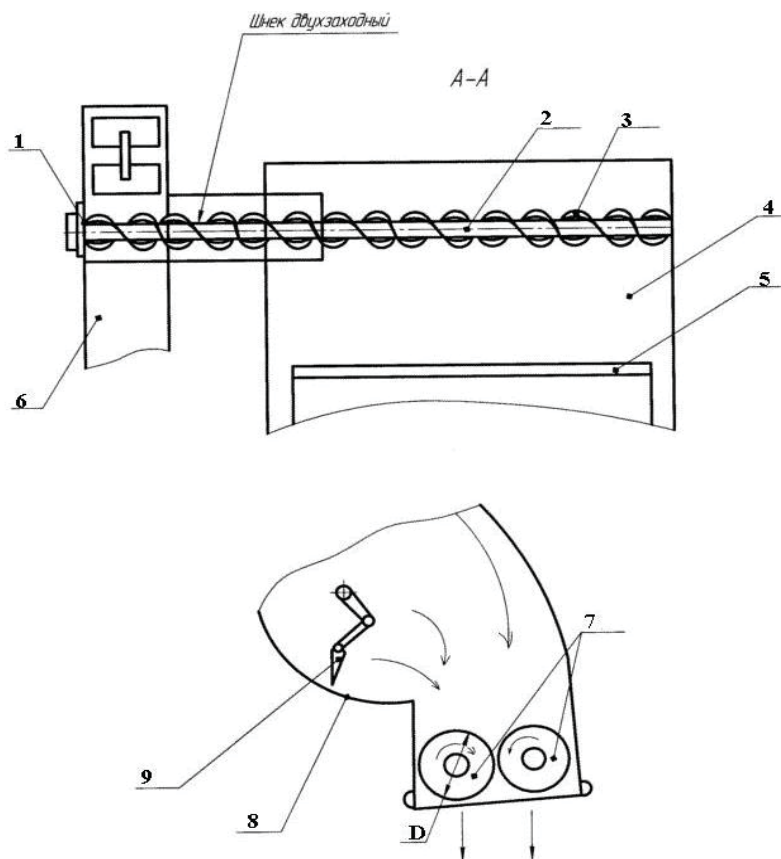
; Рис.5 Комбайн зерноуборочный гусеничный
